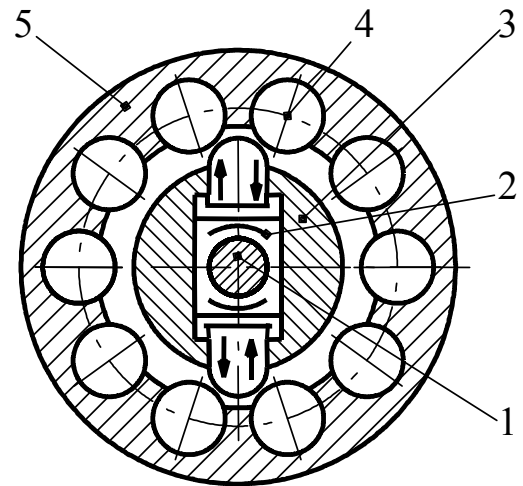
Схема ротаційно-кувальної машини: 1 – заготовка; 2 – бойок; 3 – шпиндель; 4 – ролики; 5 – обойма
